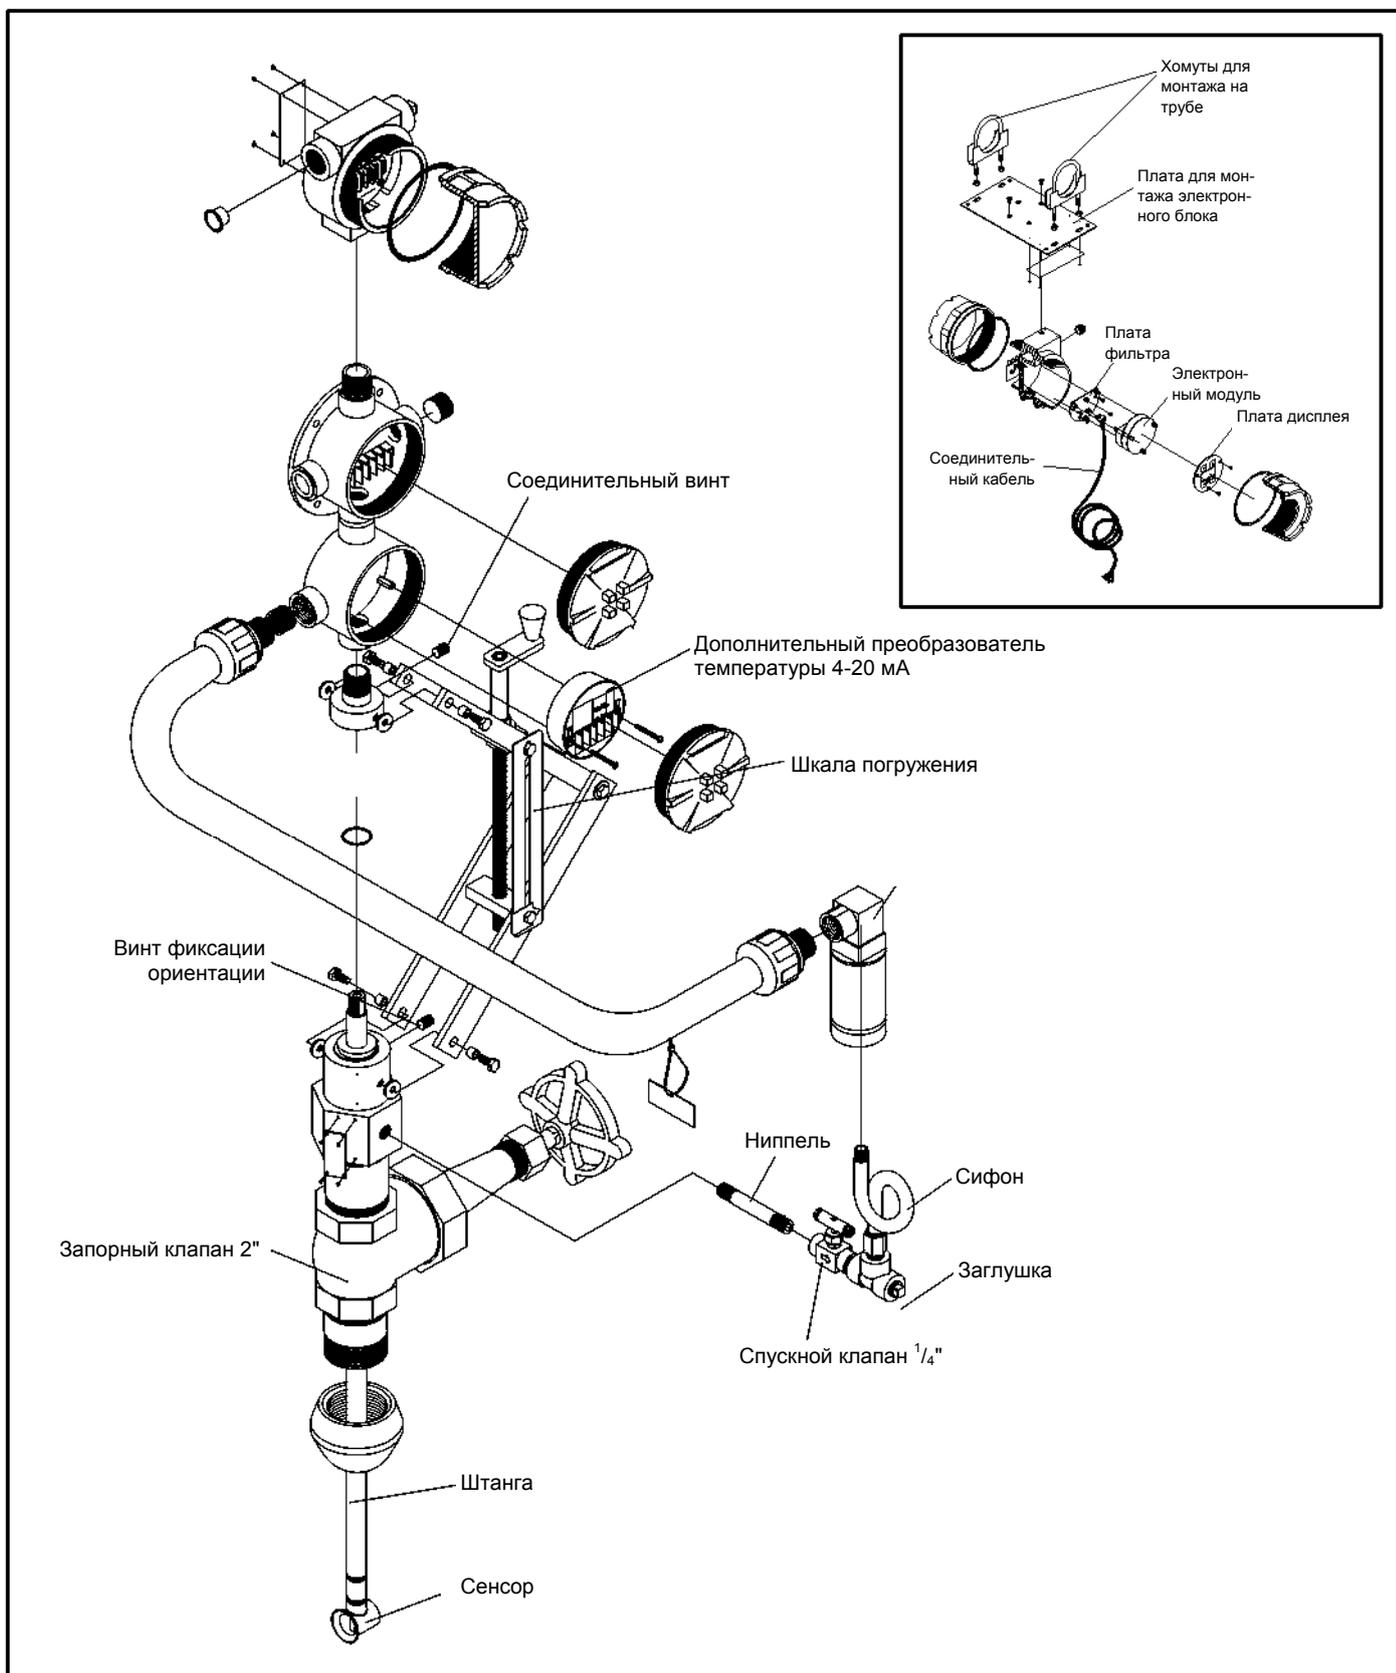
Сборочный чертеж V-Bar-600/60S раздельного исполнения
